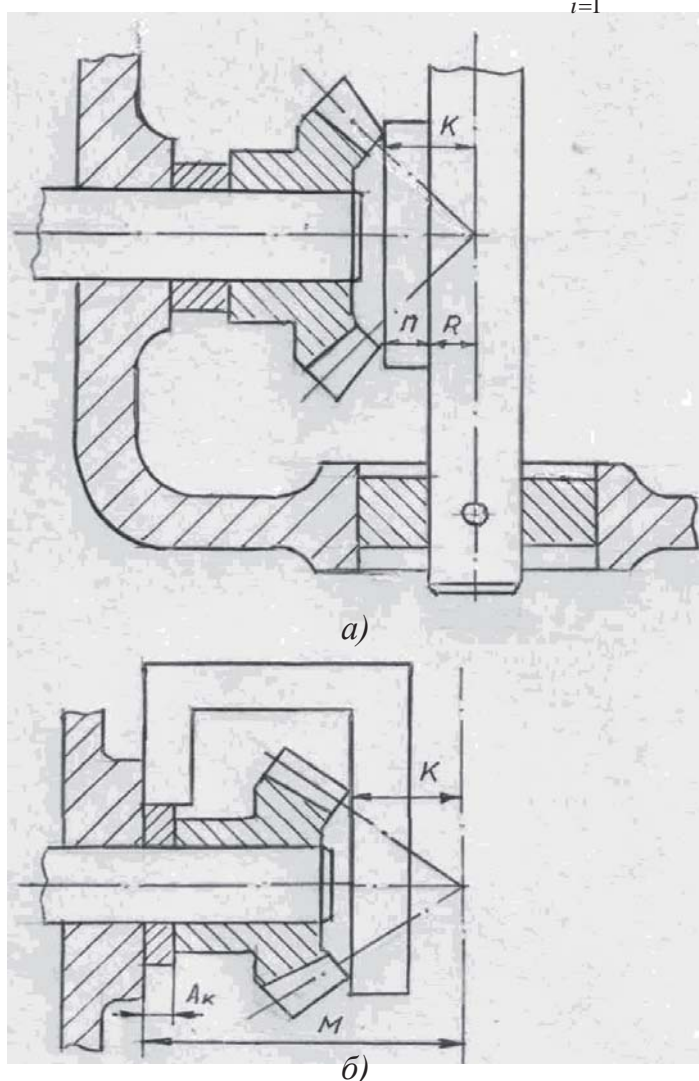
Измерение положения вершины делительного конуса при сборке конической передачи: а – эталонного валика; б – с помощью плоского калибра
